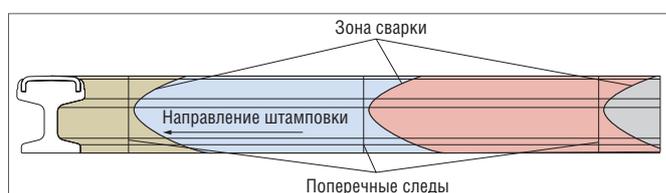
Поперечные следы матрицы при остановке пресса перед зоной сварки
